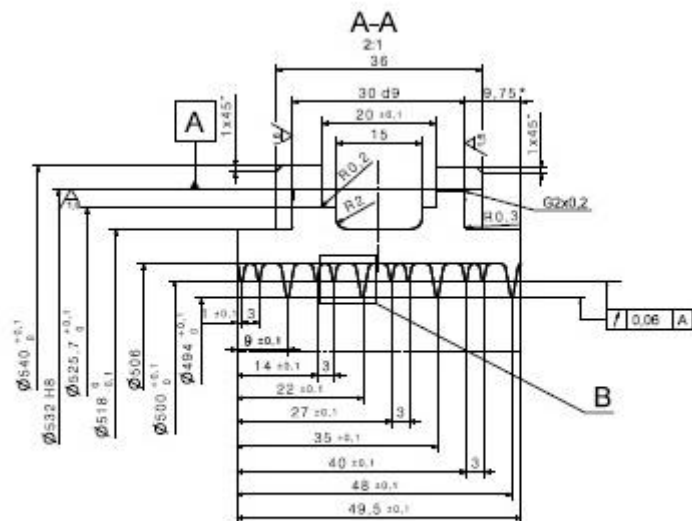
Detail břítu (ukázka detailu jednoho z provedení)
